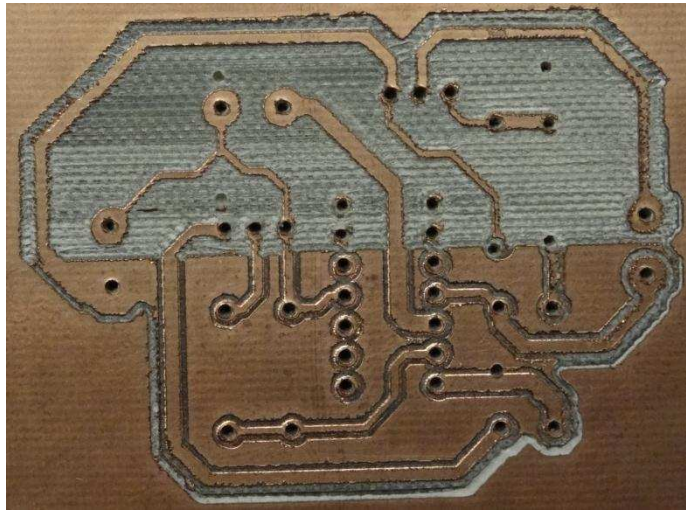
PCB con fresa cónica, broca gruesa, desbastado 50%
